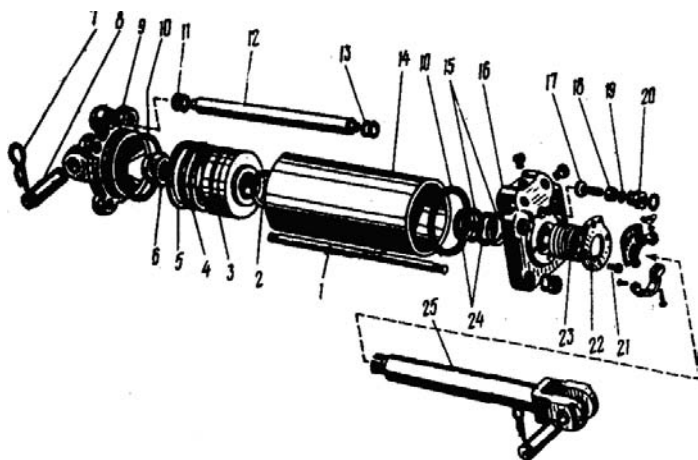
Гидроцилиндр Ц 100. 1 — шпилька; 2, 5, 10, 11, 19 и 24 — кольца; 3 — поршень; 4 и 15 — прокладки; 6 — гайка; 7 — шплинты; 8 — пальцы; 9 — задняя крышка; 12 — маслопровод; 13 — шайба; 14 — корпус; 16 — передняя крышка; 17 — клапан; 18 — втулка; 20 — корпус; 21 — болты; 22 — крышка чистиков; 23 — чистики; 25 — шток
